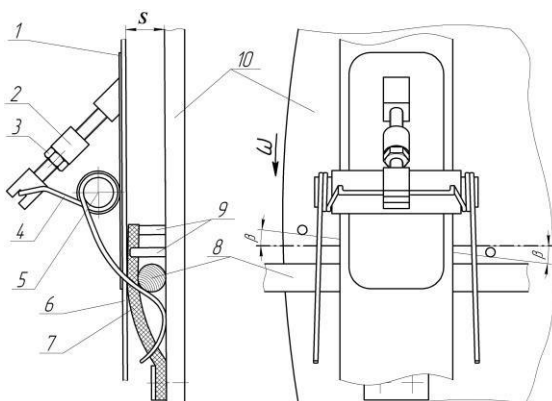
Схема орієнтуючого пристрою: 1 – основа; 2 – болт, яким регулюється притискна сила пружини на підщепи; 3 – гайка; 4 – пружина; 5 – механізм кріплення пружини; 6 – копір; 7 – захват; 8 – підщепа; 9 – упори; 10 – диск садильного апарата;  $S$  – зазор між диском та копіром.
